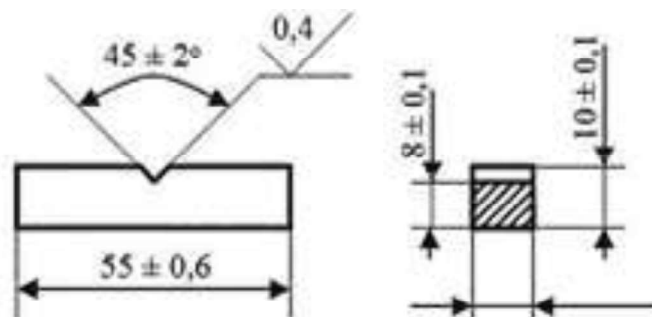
Dimensiones para la probeta del ensayo Charpy.
